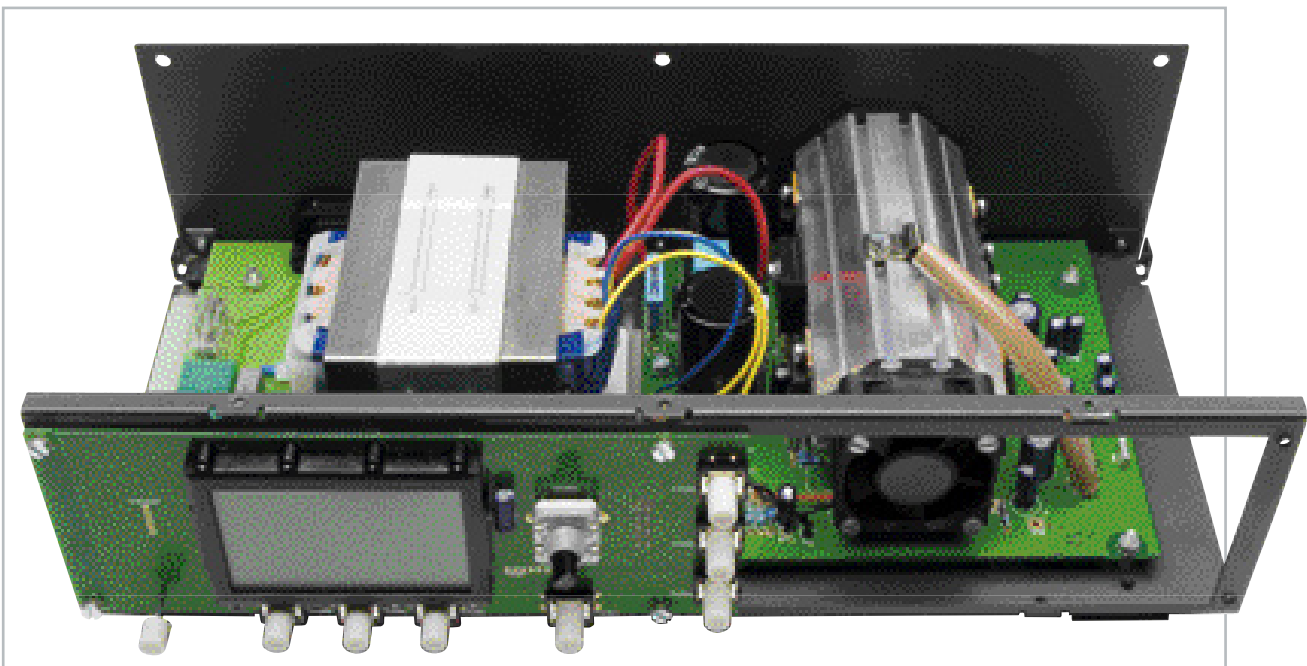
Innenansicht des fertig aufgebauten PPS 5330
